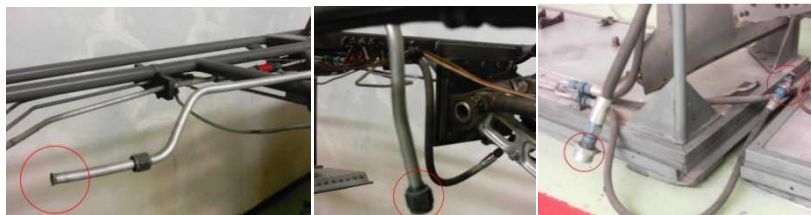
Cañerías rígidas y flexibles desconectadas
